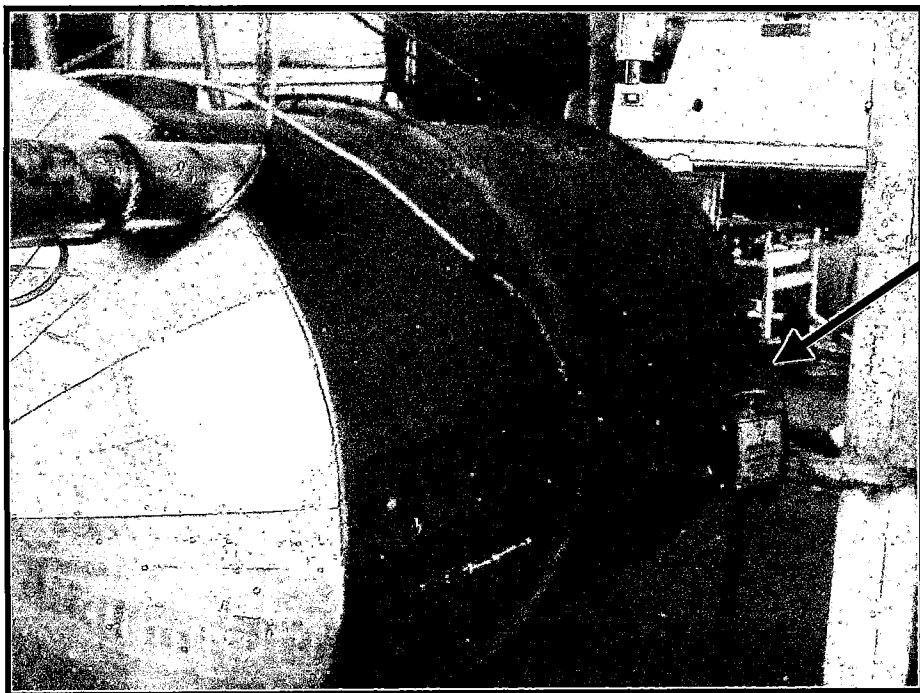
Inspección del Tanque de Tratamiento Térmico para determinar los puntos de soldaduras a someterse a las pruebas.
